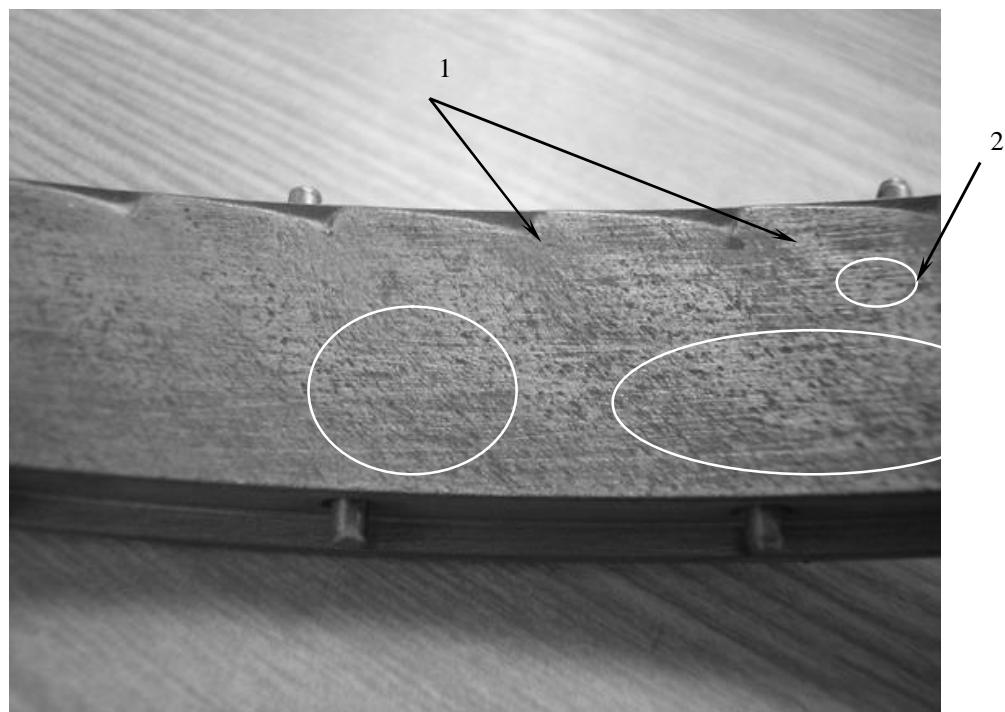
Кольцо рабочего колеса компрессора вертолетного двигателя. Дефекты: 1 – сколы; 2 – пористость
